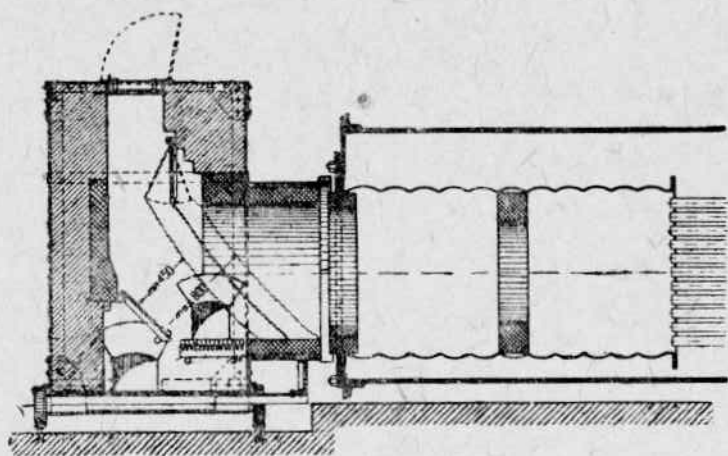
Шахтная топка для торфа и дров для локомотива с выдвигной системой трубок.
